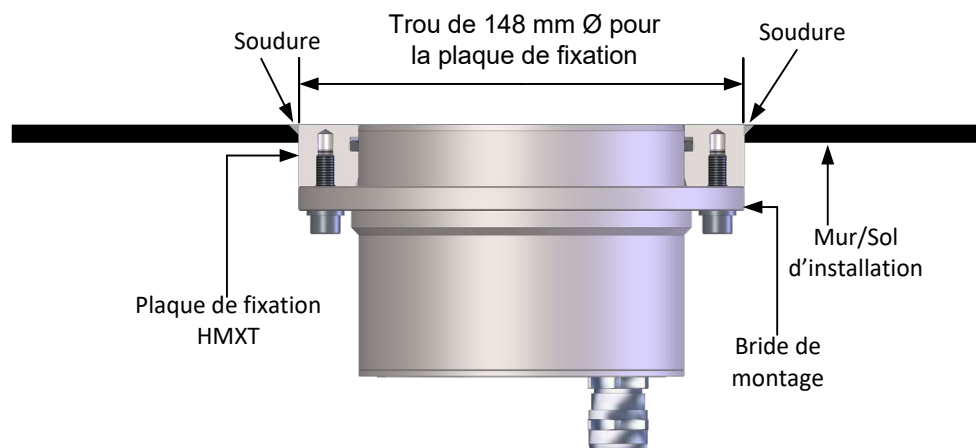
installation de la sonde (plaque de fixation installée en affleurement)
